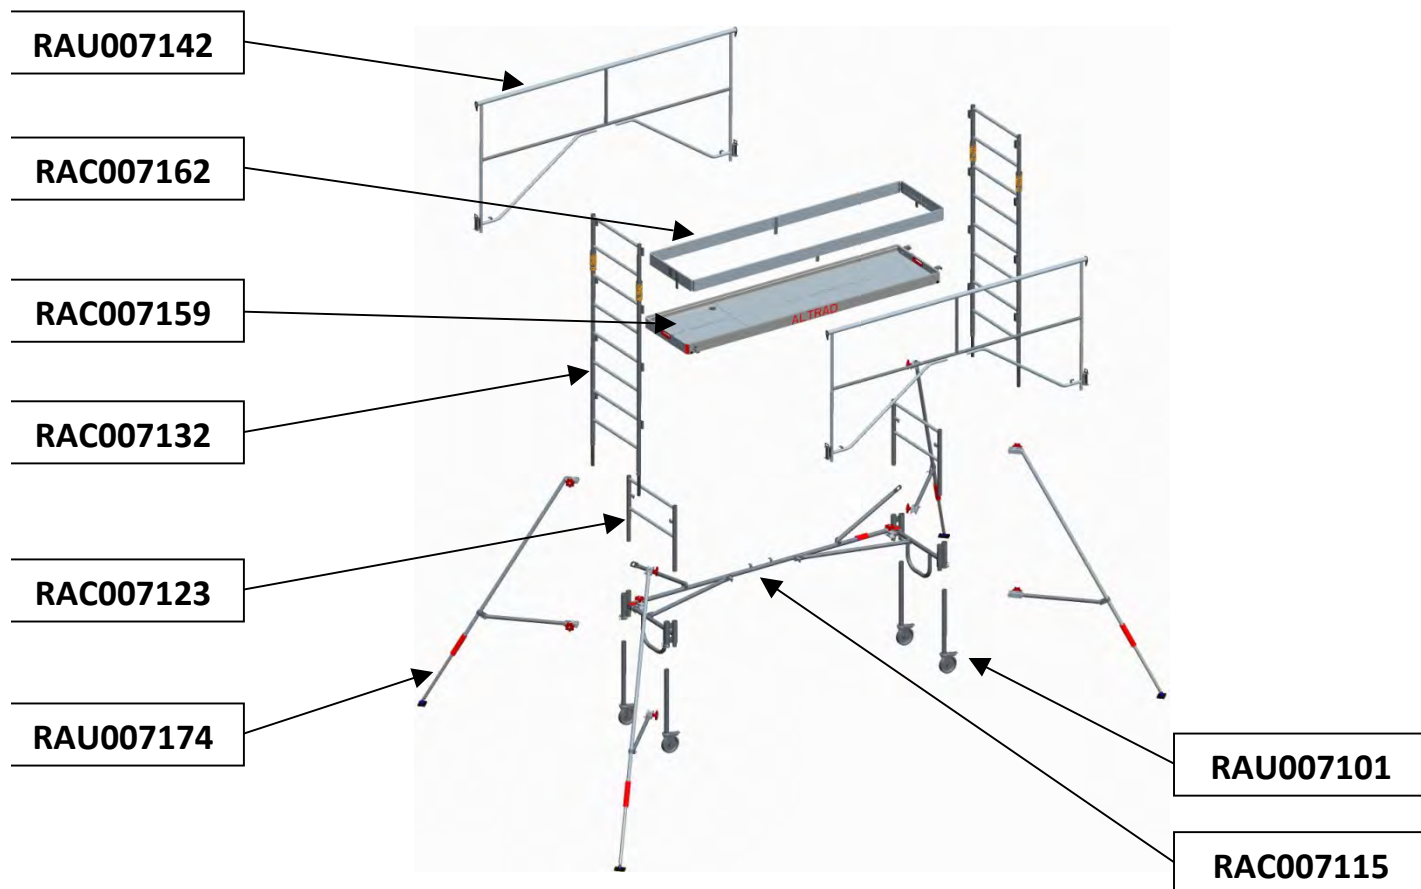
Vue d'ensemble éclatée d'un échafaudage 2m plancher (ALTEAM 35 - 250)
